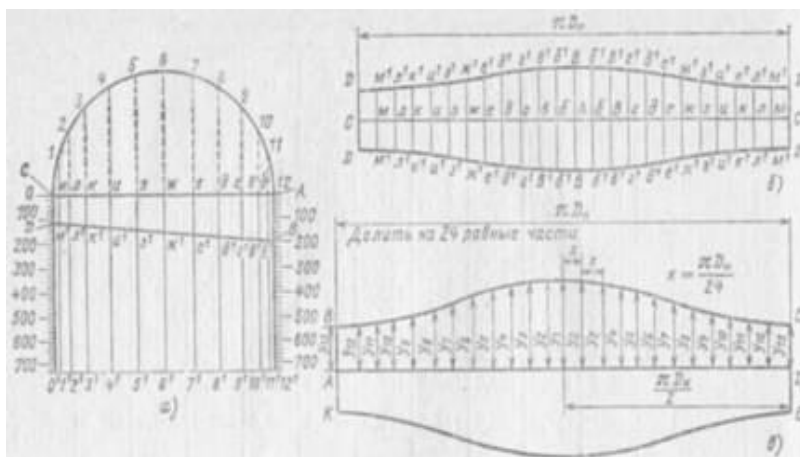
Графический способ разметки сварных отводов:
